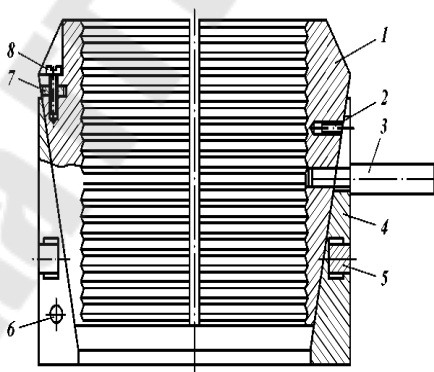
Клиновидная одноступенчатая подвеска: 1- плашки; 2-винты; ручки; 4-корпуса; 5- полукольца; 6- штифты
